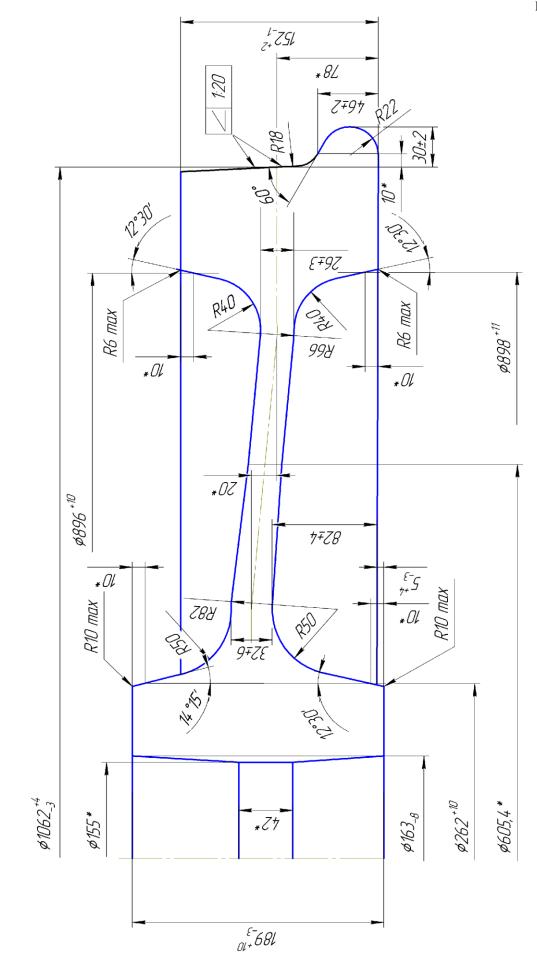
Колесо Ø 1062 мм с черновой механической обработкой, для Ø 1050 мм по чертежу № КР-0032-16. Масса колеса 532 кг
